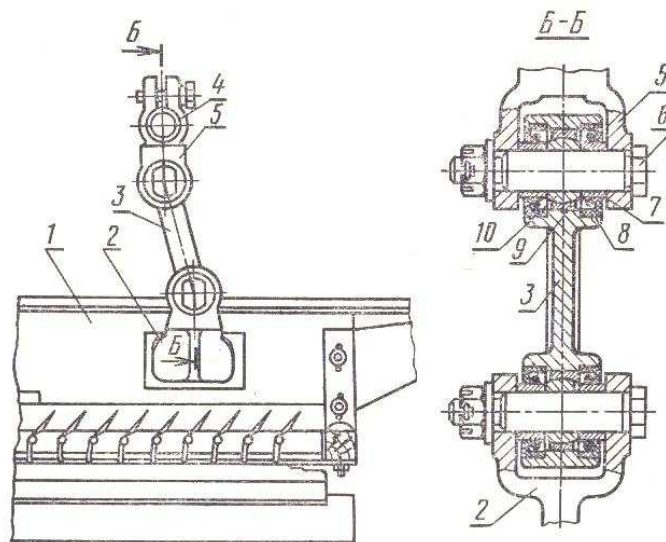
Задняя подвеска решетного стана комбайна СК-6: 1 - боковина решетного стана; 2, 5 – кронштейны; 3 – задняя подвеска; 4 – трубчатый вал; 6 – болт; 7 – распорная втулка; 8 – уплотнительное кольцо; 9 – обойма сферического подшипника; 10 – сферическое кольцо
